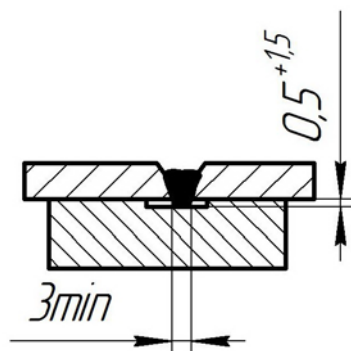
Эскиз конструктивных элементов продольного сварного шва обечайки после сварки первого прохода
